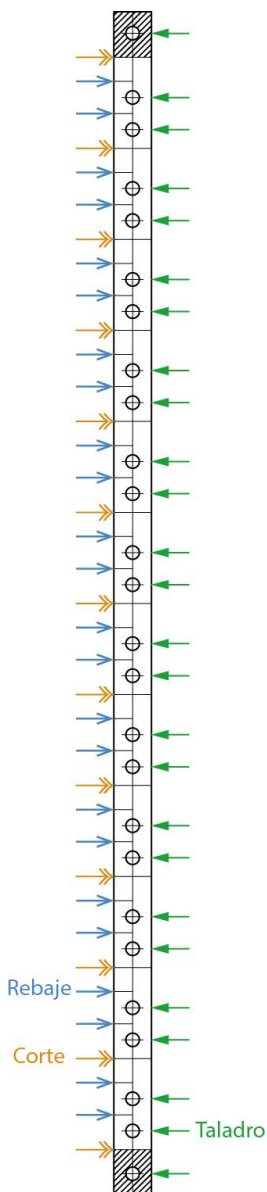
· Marcado de las barras usando el plano de fabricación como plantilla.
